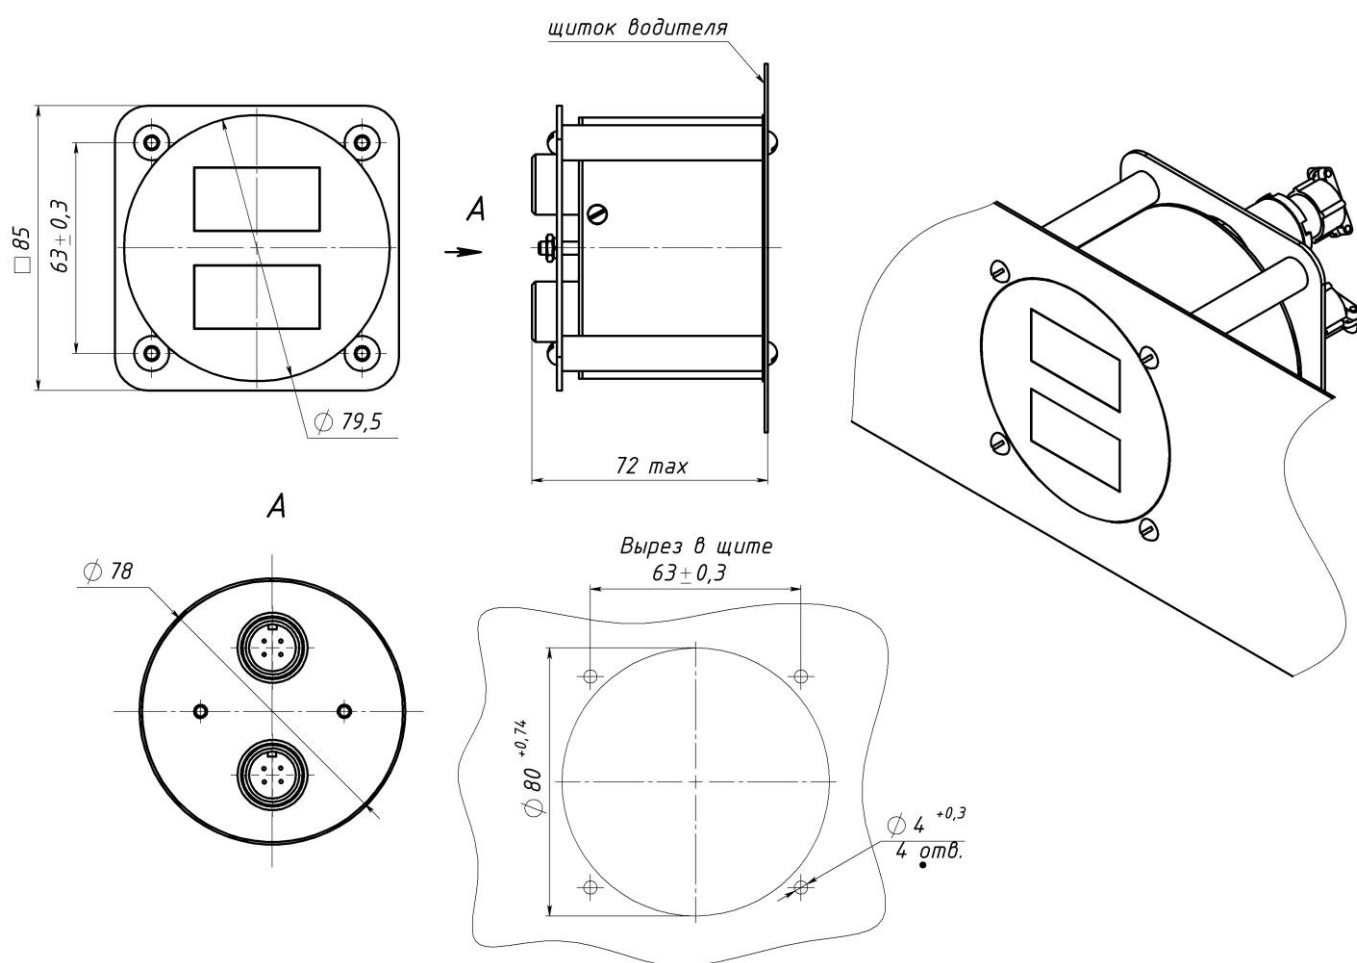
Габаритные и присоединительные размеры прибора ТУЭ-2Ц
